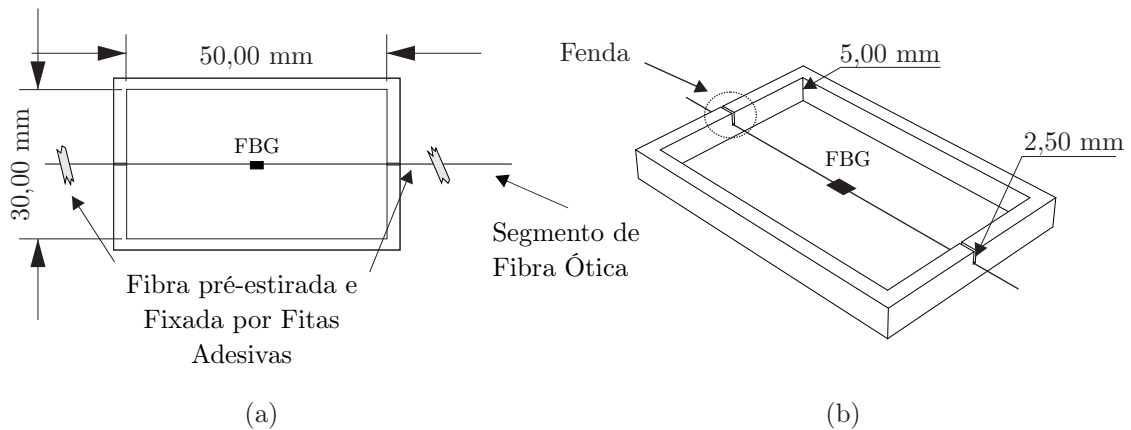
Representação esquemática do molde utilizado para encapsular uma FBG. (a) Vista Superior e (b) Vista Isométrica.
